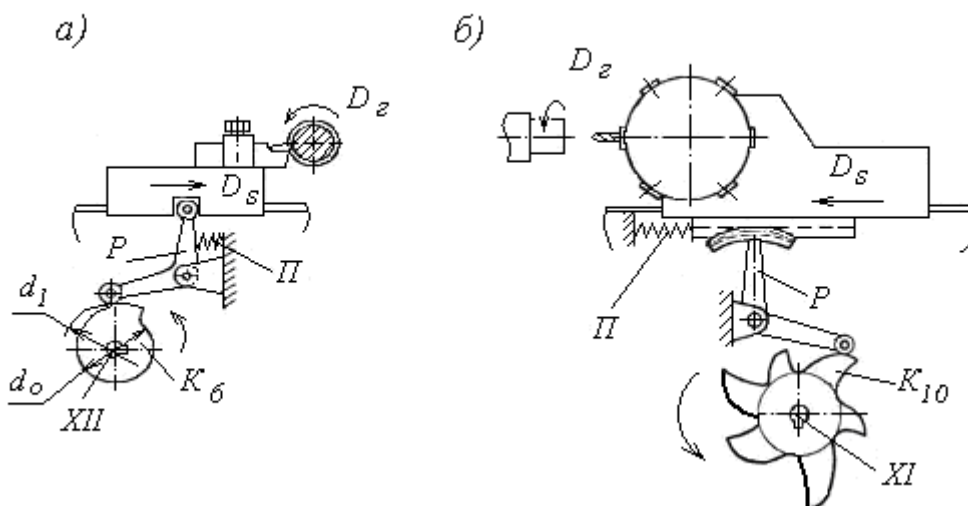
Механизмы перемещений переднего (*a*) и револьверного (*б*) суппортов
